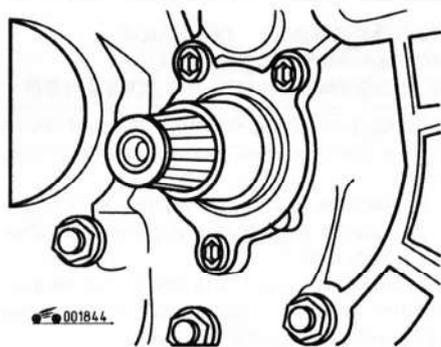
Установка направляющей втулки подшипника выключения сцепления
